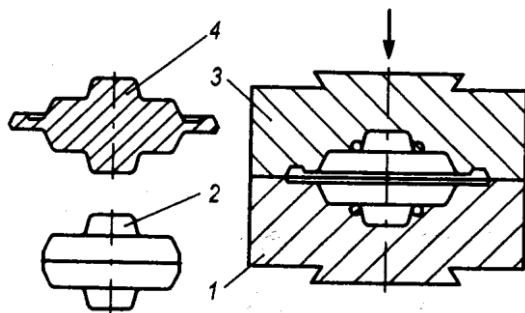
Схема об'ємного штампування: 1 – нижня частина штампа; 2 – кованка; 3 – верхня частина штампа; 4 – кованка з невідокремленим об'ємом
